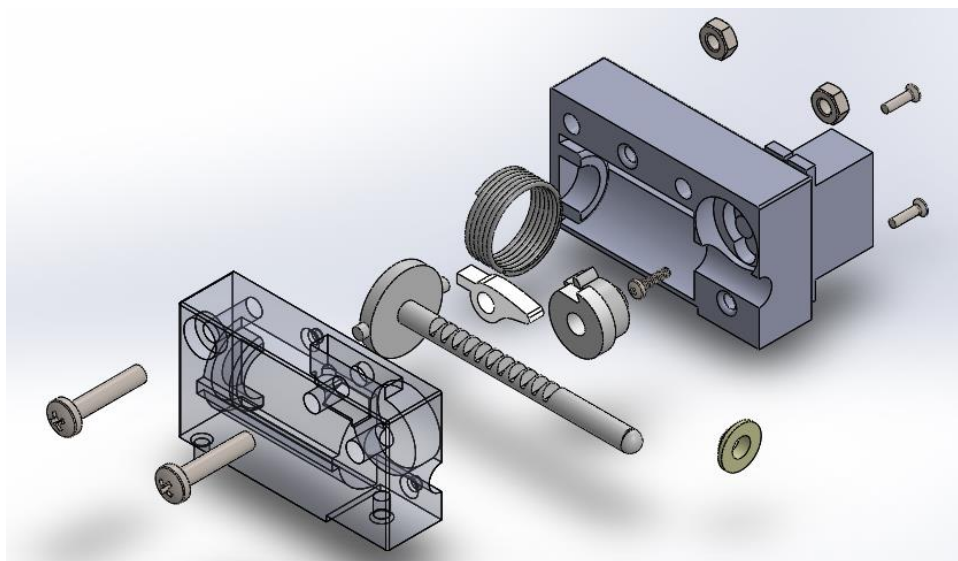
Desenho de conjunto do atuador dimensionado.
